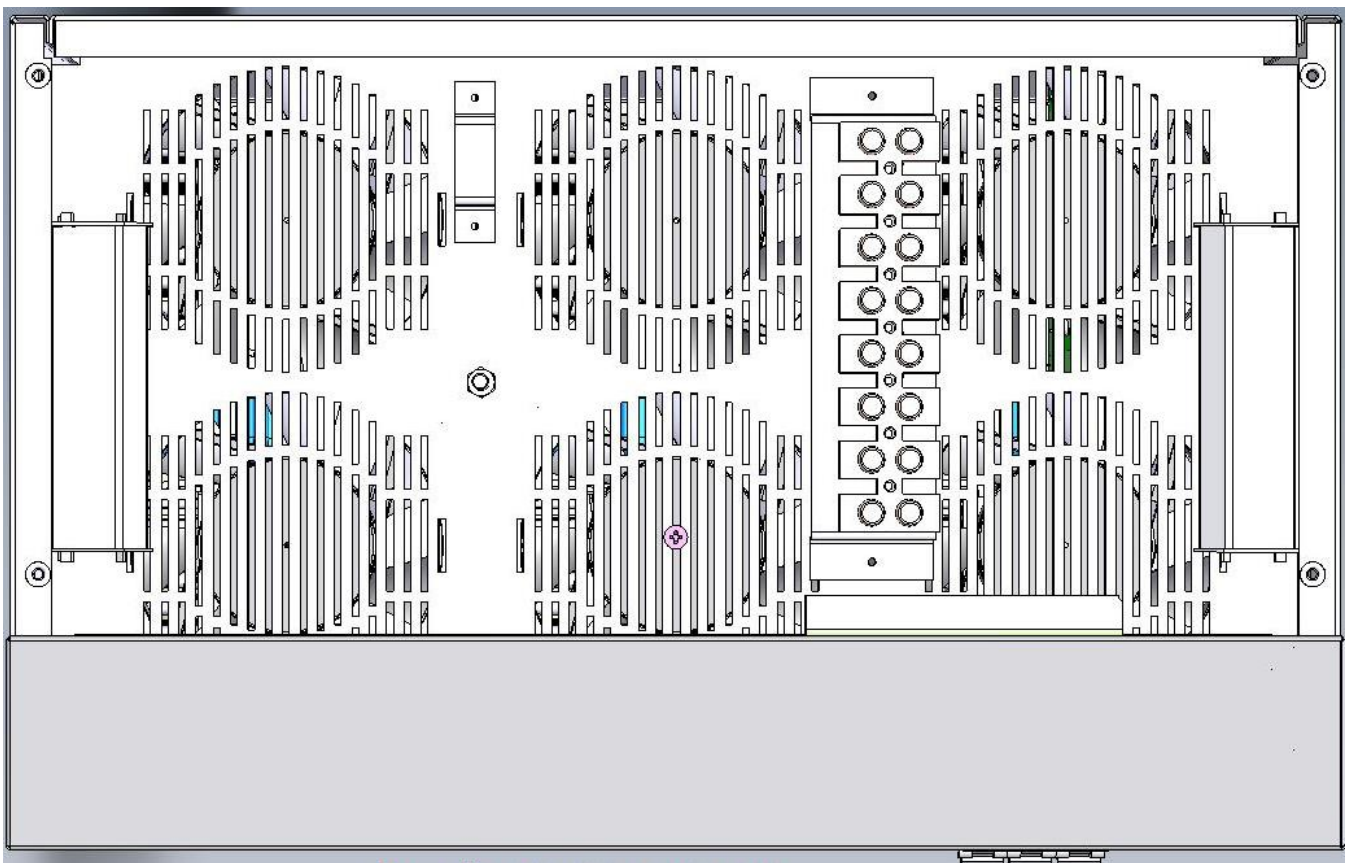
Зовнішній вигляд верхньої частини стабілізатора
